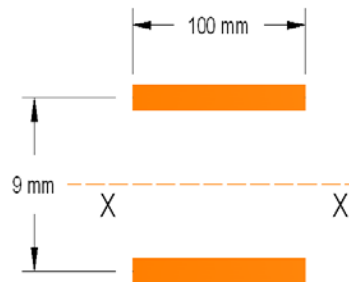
Geometría de la soldadura a realizar
